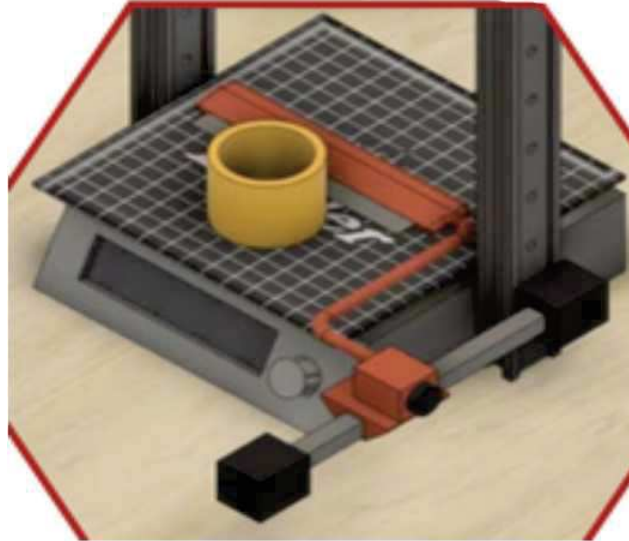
Пристрій знаходиться у положенні скидання друкованої 3D деталі
